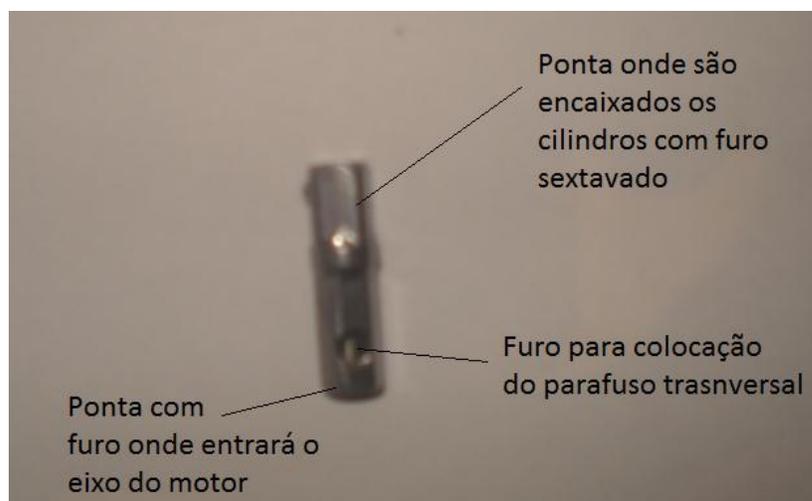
Peça de conexão entre o eixo do motor e as ferramentas.
